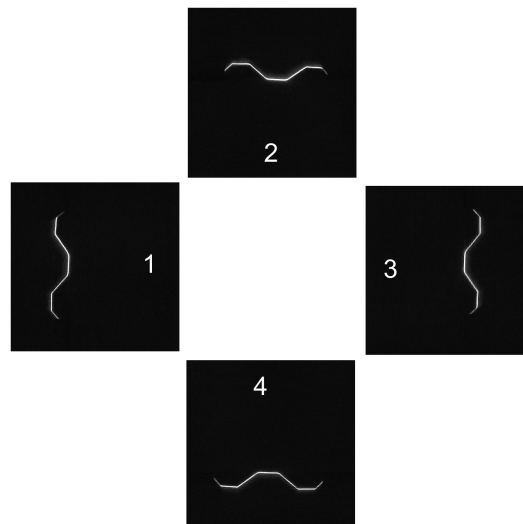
Imágenes tomadas por las 4 cámaras para un perfil metálico.
